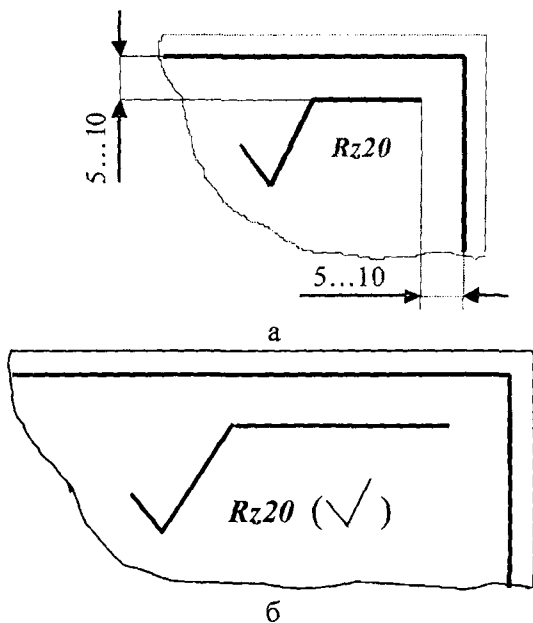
Примеры обозначений параметров одинаковой шероховатости
